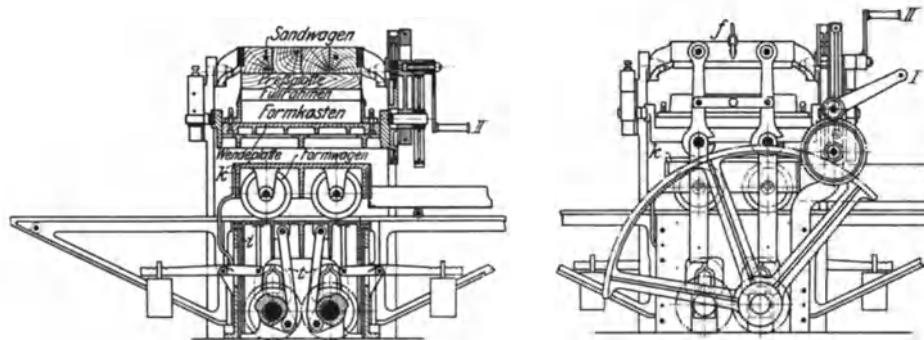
und 67. Preßformmaschine, Bauart Sebold 1872.
